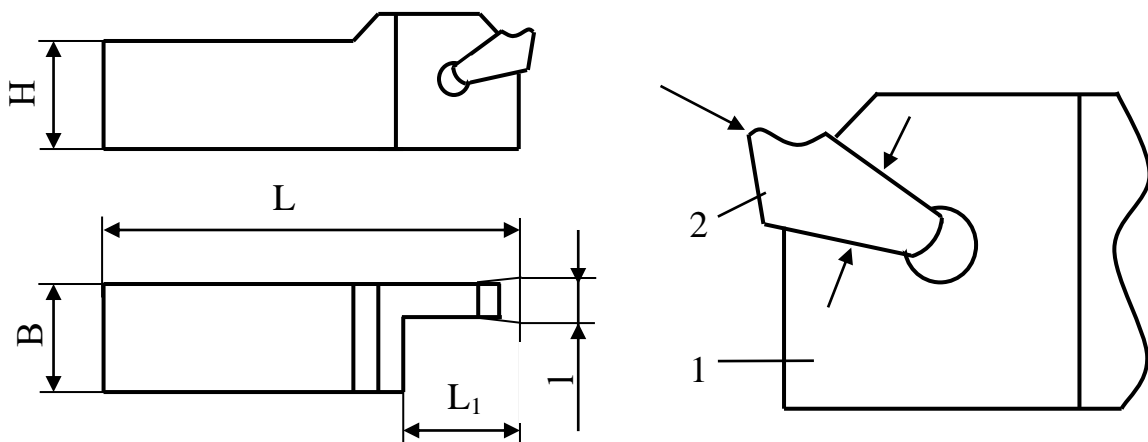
Збірний відрізний різець T-MAX Q-Cut
